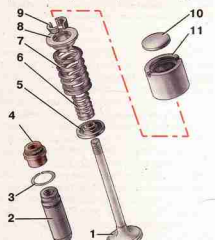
Детали механизма привода клапанов: 1 – клапан; 2 – направляющая втулка; 3 – стопорная колодка; 4 – маслоотражающий колпачок; 5 – опорная шайба пружины; 6 – внутренняя пружина; 7 – наружная пружина; 8 – тарелка пружины; 9 – сухарь; 10 – регулировочная шайба; 11 – толкатель
